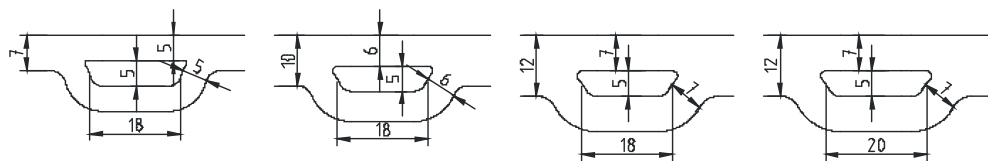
Querschnitte der breitesten FracTherm®-Kanäle Typ E
